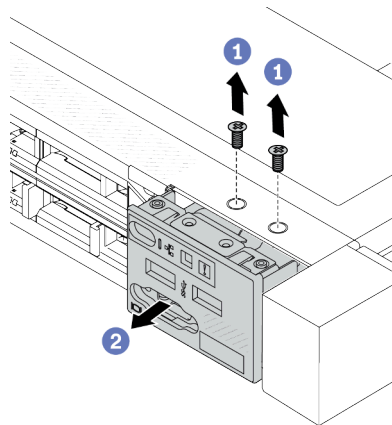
Remover um módulo de E/S frontal no chassi de 2,5 pol.
